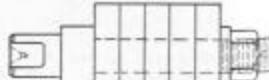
Mandril de porca para acabamento de discos de engranagem
